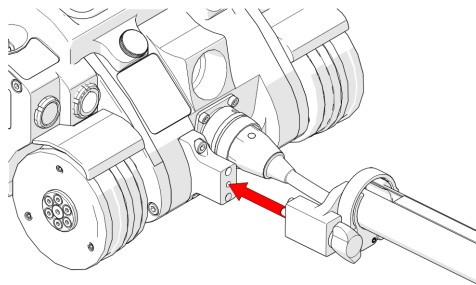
Ausrichten auf die Versorgungsleitung
